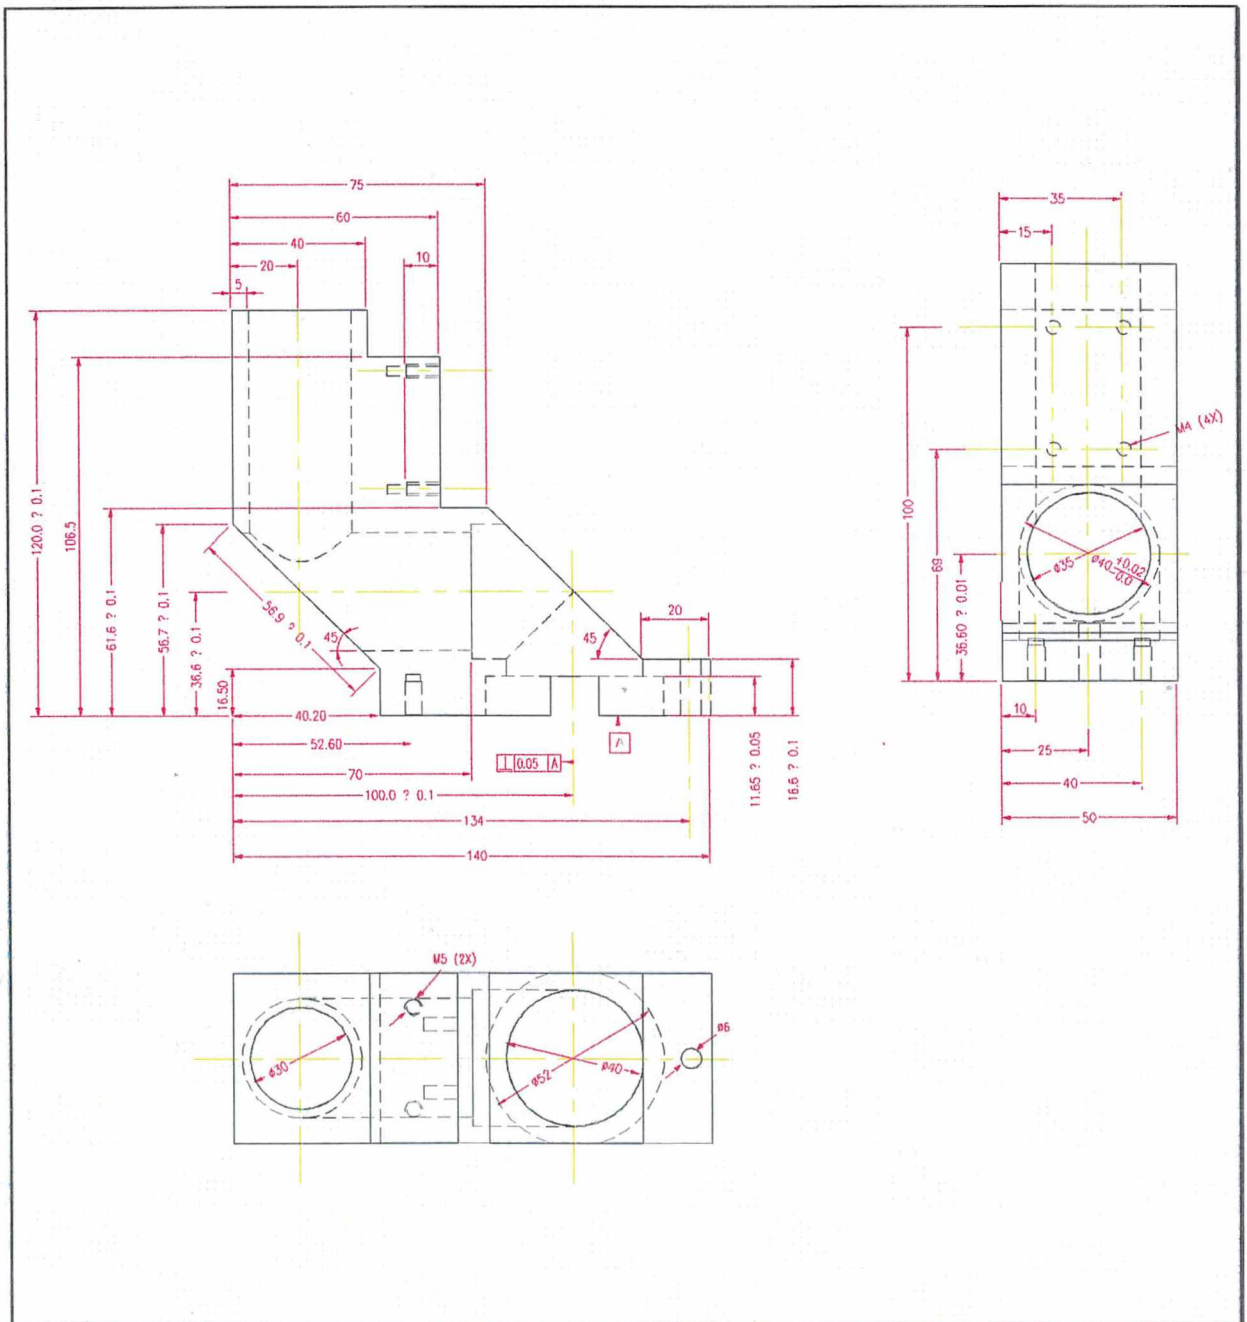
Detalhe da estrutura monobloco que integra os diversos elementos ópticos
